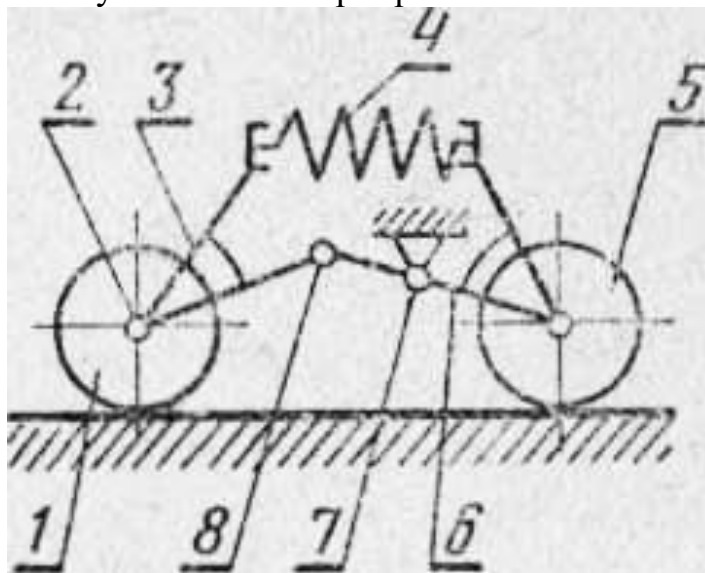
Схема балансирующей каретки гусеничного трактора:
